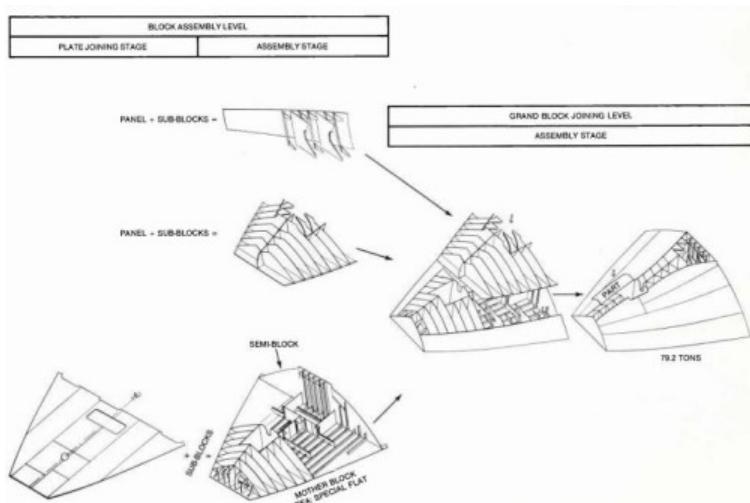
Semi-block and Block Assembly pada Bottom Wing, Side Shell with Hopper, and Transverse Hopper in Cargo Hold
